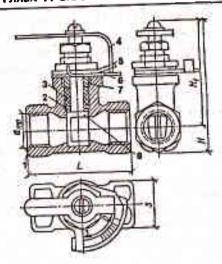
Кран двойной регулировки типа КДР: 1 — корпус; 2 — кольцо оборнов; 3 — набивка сальника; 4 — ручки; 5 — регулятор; 6 — указатель; 7 — пробка
